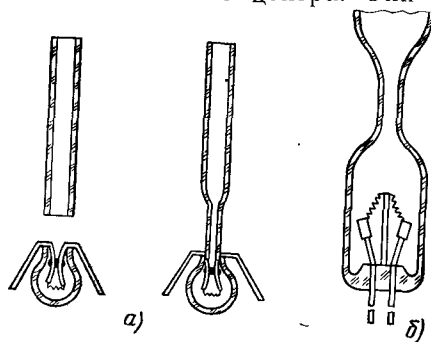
Схемы заварки и откачки лампы с бусинковой ножкой
